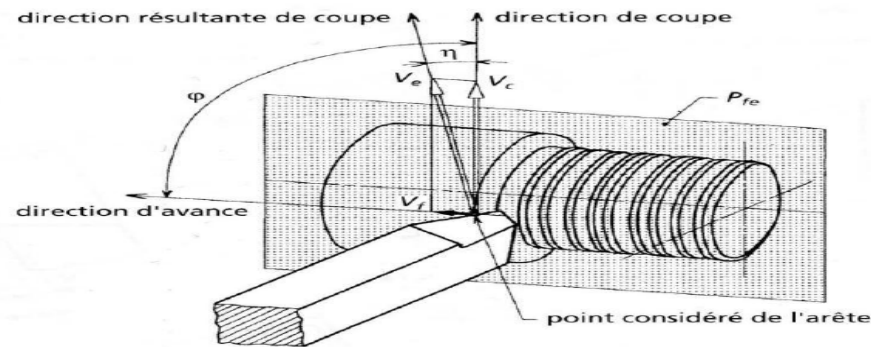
Mouvement relatif outil/ pièce en tournage [9].
